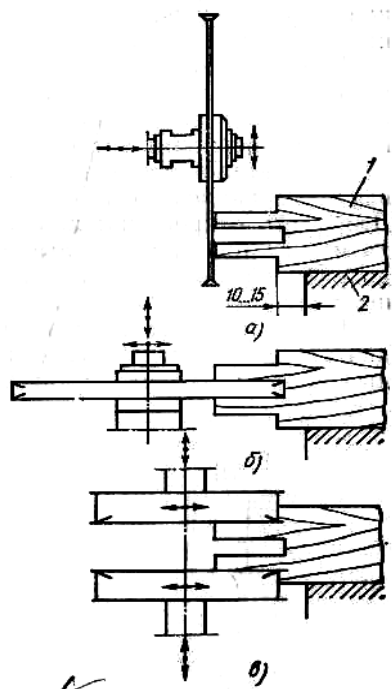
Настройка режущих инструментов шипорезного станка для рамных шипов: а – пилы; б – дисковой фрезы; в – шипорезных фрез; 1 – эталонная деталь; 2 – стол каретки
